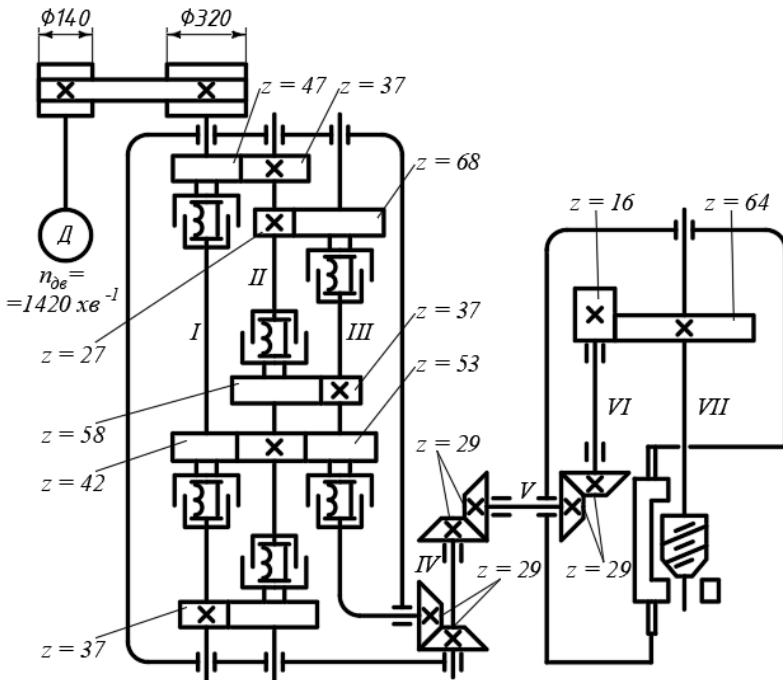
Кінематична схема коробки швидкостей зубофрезерного верстата (приклад)
